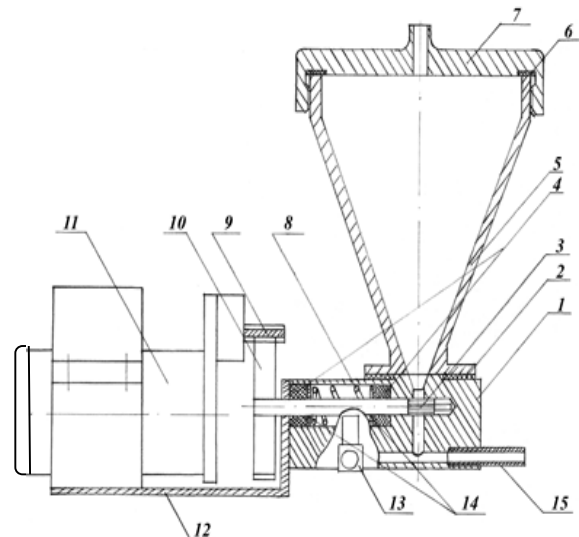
Конструкція порошкоживильника: 1 - корпус; 2 - ротор; 3 - гумова прокладка; 4 - сальник; 5 - бункер; 6 - гумова прокладка; 7 - кришка; 8 - пружина; 9 - вал-шестерня; 10 - шестерня; 11 - електродвигун; 12 - кронштейн; 13 - трійник; 14 - шайба; 15 - штуцер
